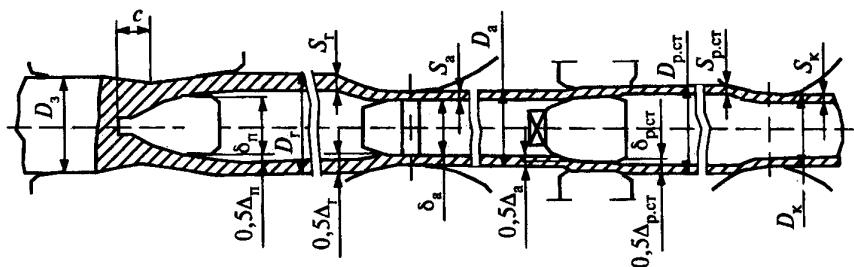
Схема изменения геометрических размеров заготовки при прокатке на ТПА с автоматическим станом
